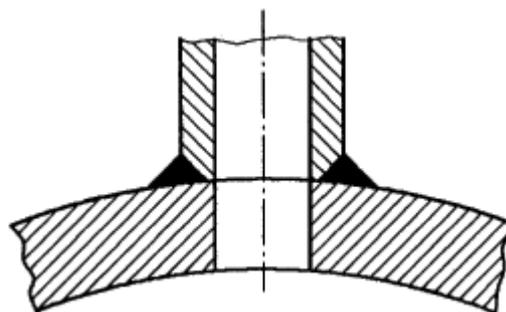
Приваривание патрубка дополнительного присоединения
